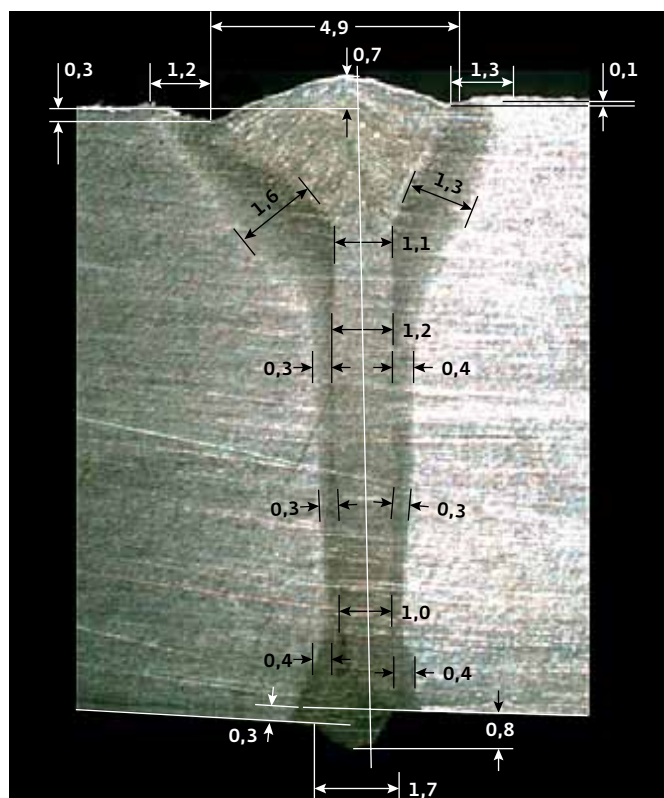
Сварочная ванна при сварке на оптоволоконной лазерной установке ( $P=10$  кВт)
